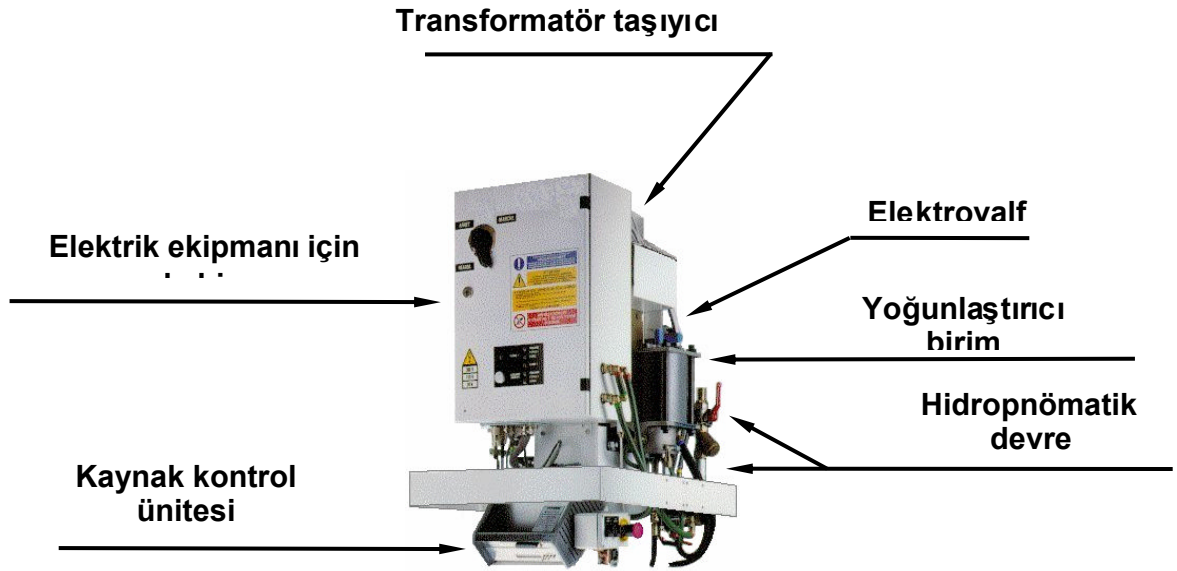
Askılı Kaynak Makinası Taşıyıcı Profil
